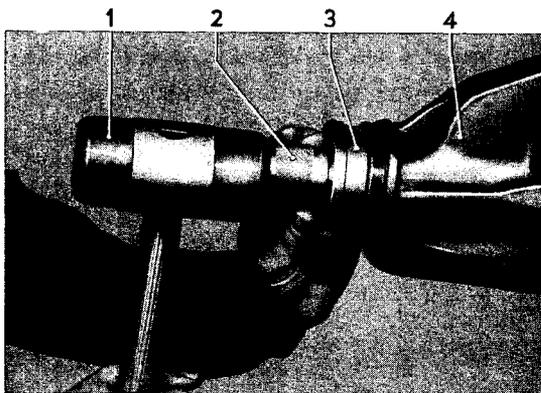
Dichtring für Antriebkegelrad einschlagen
